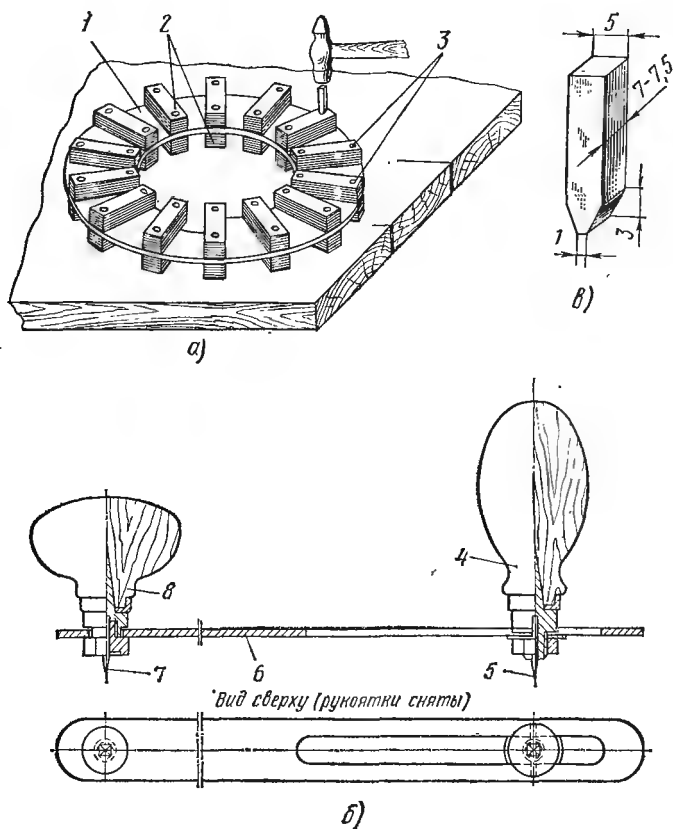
Сборка ярмовой изоляции обмотки трансформатора (а), ручной шайборез (б) и картонная заклепка (в):
